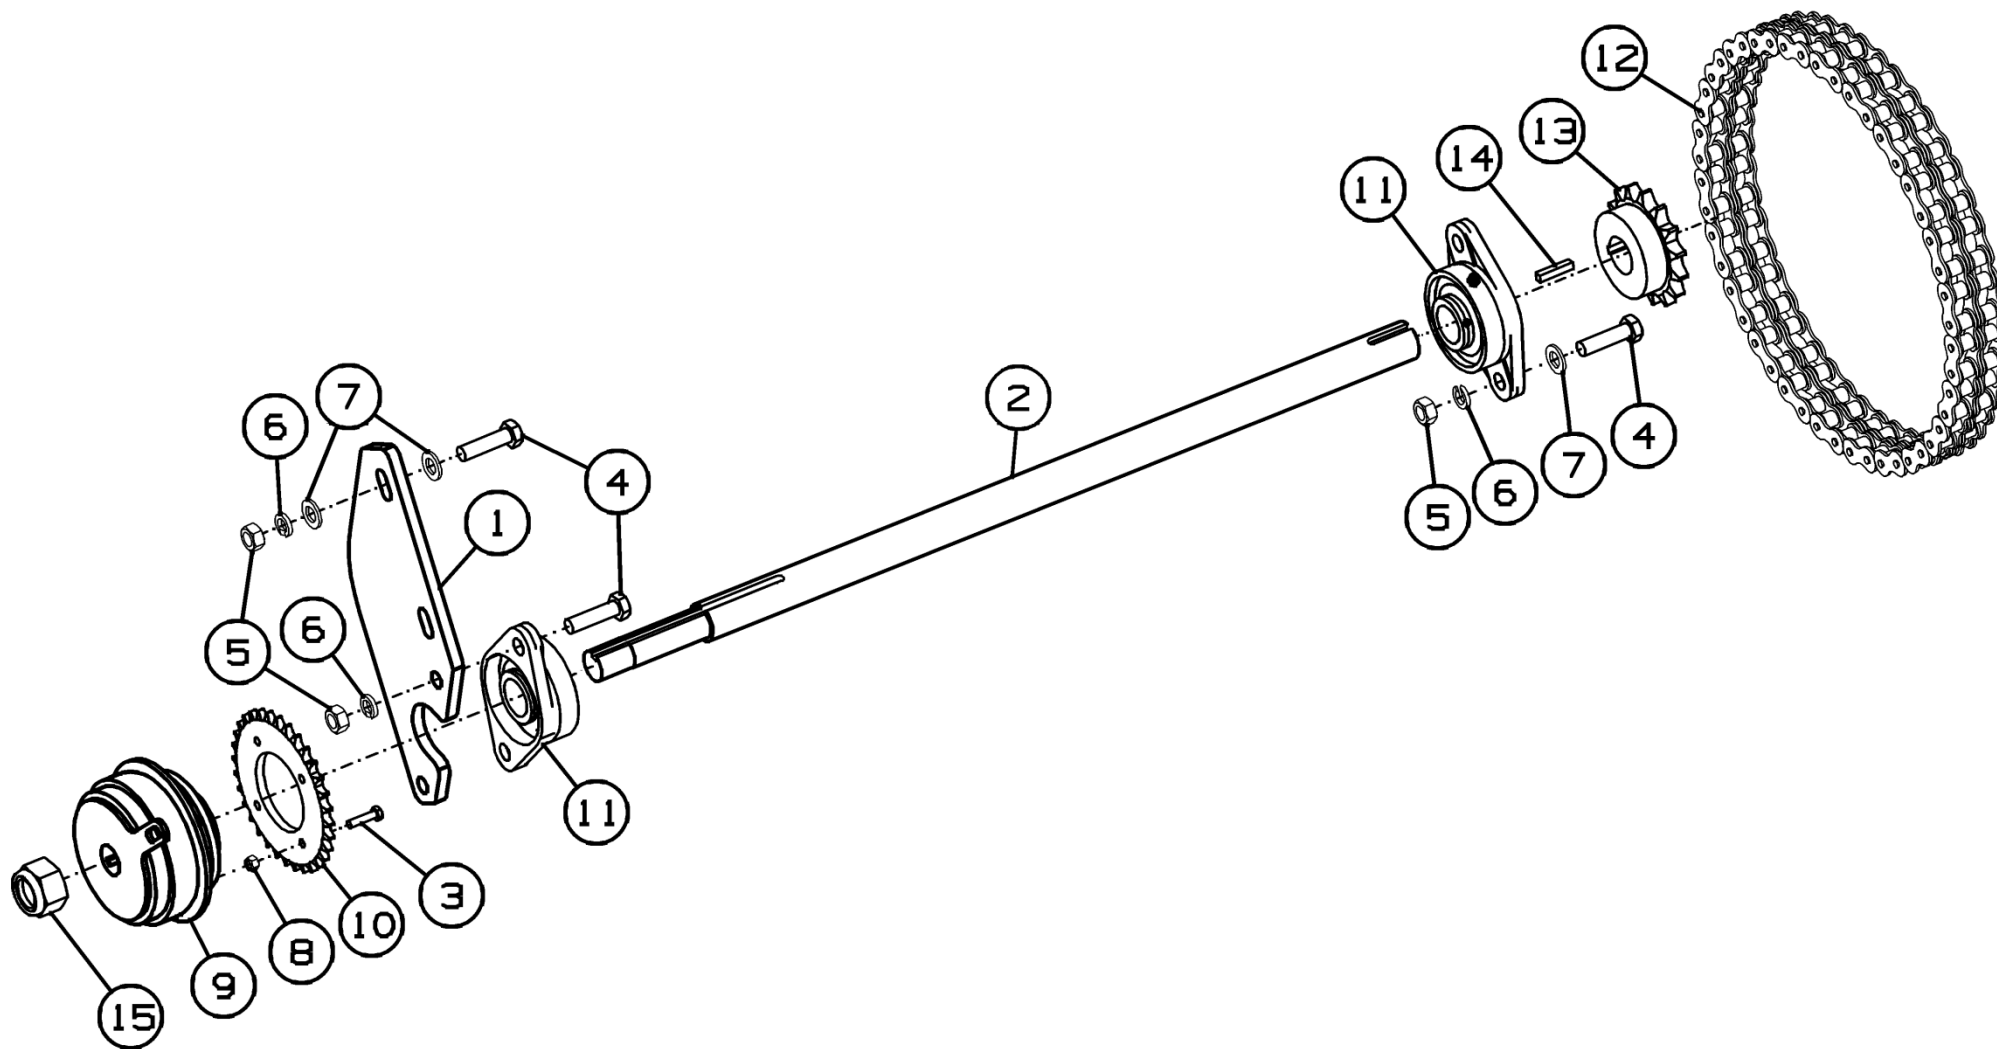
Главный привод в сборе АТ-11.42.200
